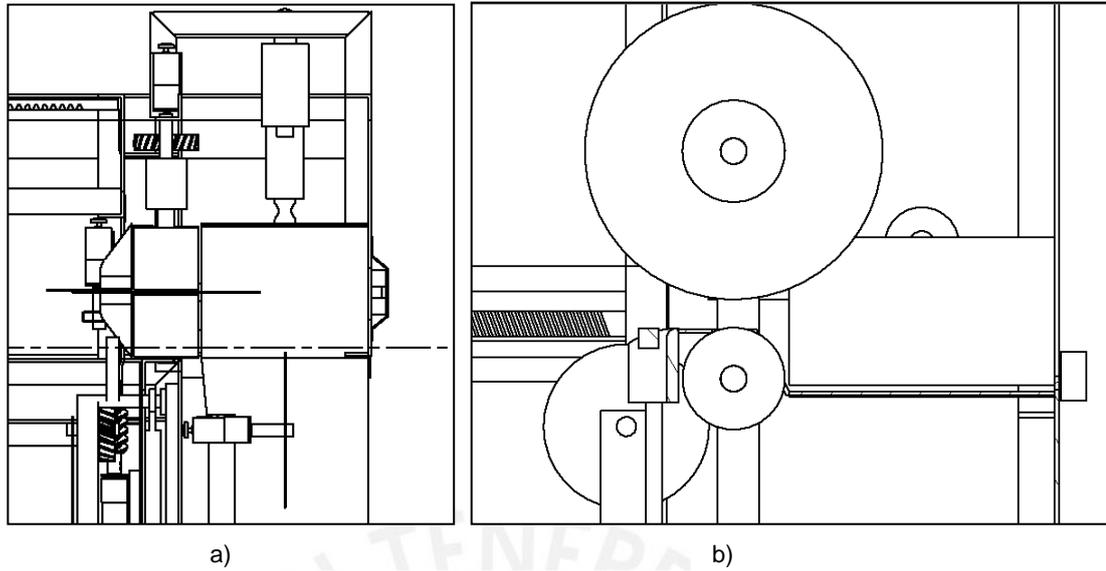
En a) se detalla el plano de planta del sistema de tres cortes y en b) es un plano seccionado donde se aprecia solo dos cortes
